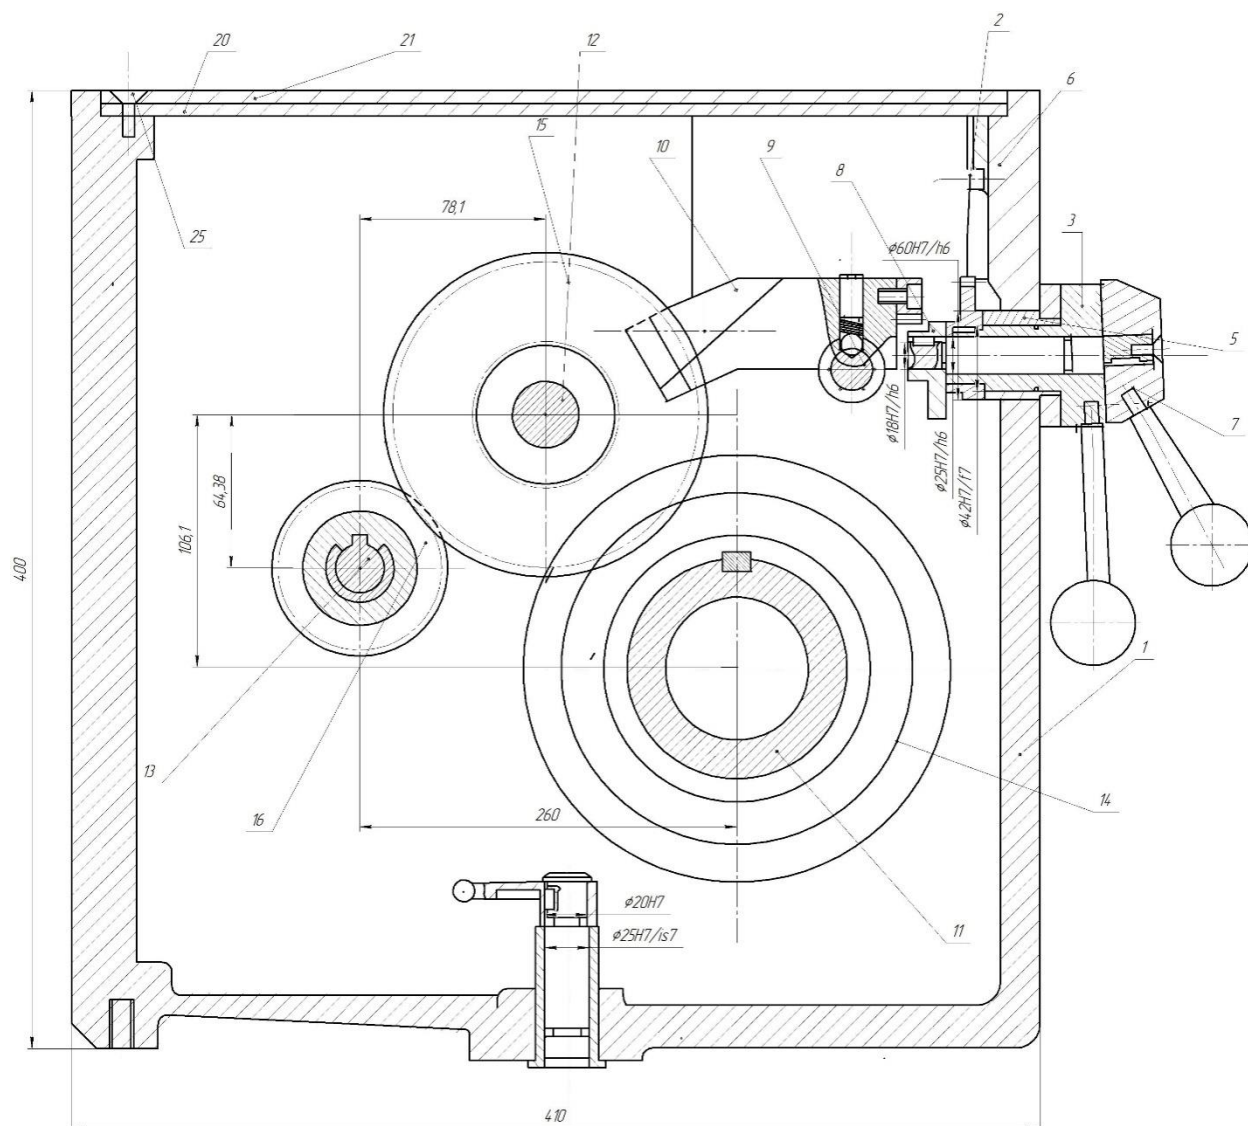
Згортка модернізованої коробки швидкостей.
